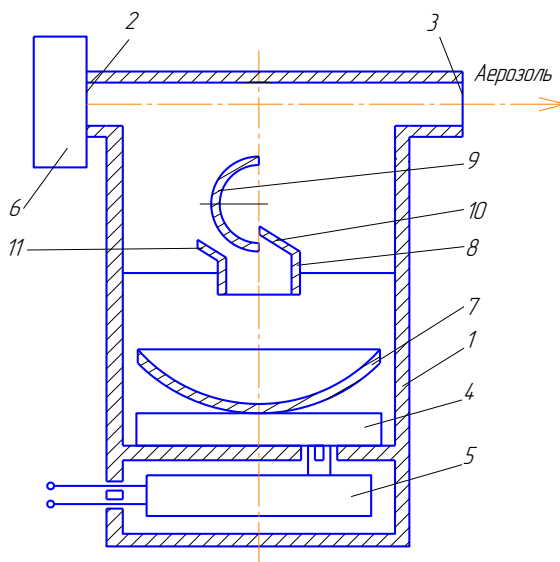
Диспергатор з акустичними лінзами: 1 – корпус; 2,3 – вхідний і вихідний отвори; 4 – п'єзоелемент; 5 – генератор; 6 – вентилятор; 7,9 – лінзи; 8 – направляюча трубка; 10-11 – пелюстки
